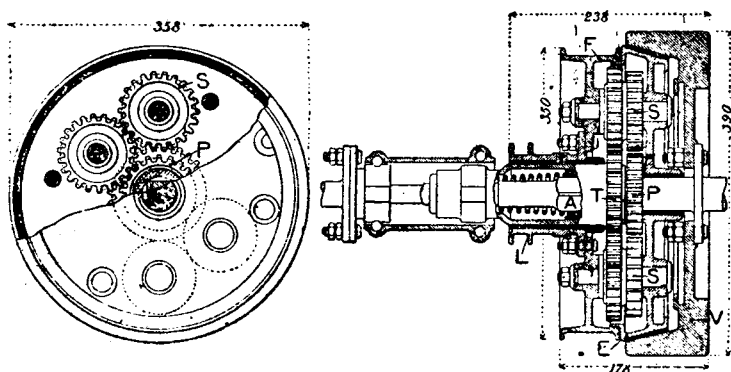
Механизм перемены вращения и разобращения двигателя отъ винта—съ цилиндрическими зубчатками вмѣсто коническихъ. Механизмъ допускаетъ уменьшеніе числа оборотовъ винта сравнительно съ двигателемъ при обратномъ вращеніи.—*V* маховикъ двигателя.—*E*, конусъ сцѣпленія.—*P*, зубчатка, насаженная на концѣ колычаго вала двигателя.—*S*, зубчатка на промежуточной оси, вращающаяся лишь при затормаживаніи барабана *F* и одновременномъ освобожденіи конуса *E*.—*T*, зубчатка на концѣ гребного вала.—*A*, квадратъ, допускающій отодвиганіе конуса посредствомъ закраинъ втулки *L*.—Кромѣ обратнаго вращенія, получается уменьшеніе числа оборотовъ винта при обратномъ ходѣ. (Сист. Демаре-Моранъ).
